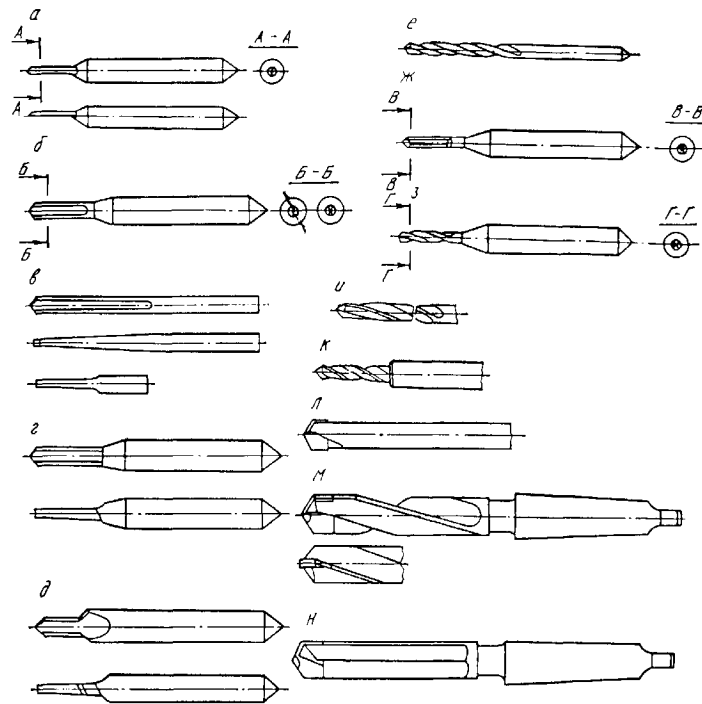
Типы мелкогабаритных быстрорежущих (а—з) и твердосплавных (и—н) сверл
